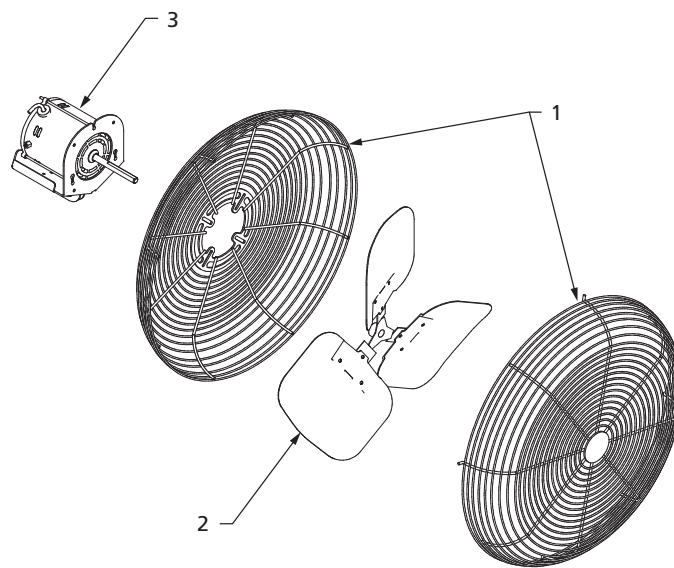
Pièces de rechange pour les ventilateurs industriels haut rendement assemblés
